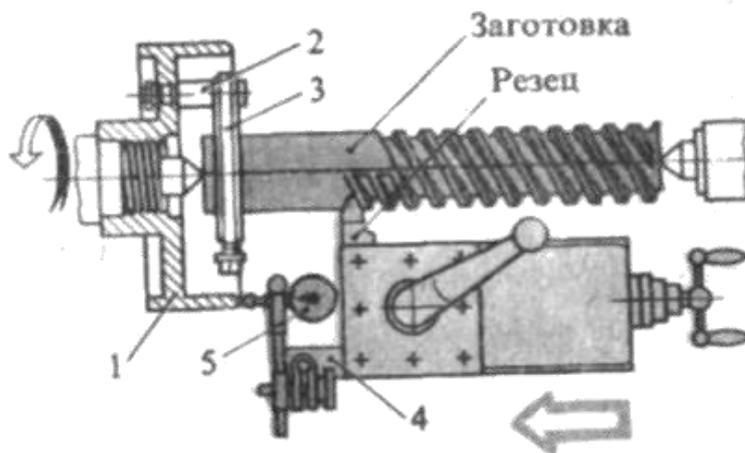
Нарезка многозаходной резьбы с делением способом перемещения резца (смещением верхних салазок суппорта с контролем шага по индикатору) 1- планшайба; 2- 2 палец; 4 3- хомутик; 4- держатель; 5- индикатор
